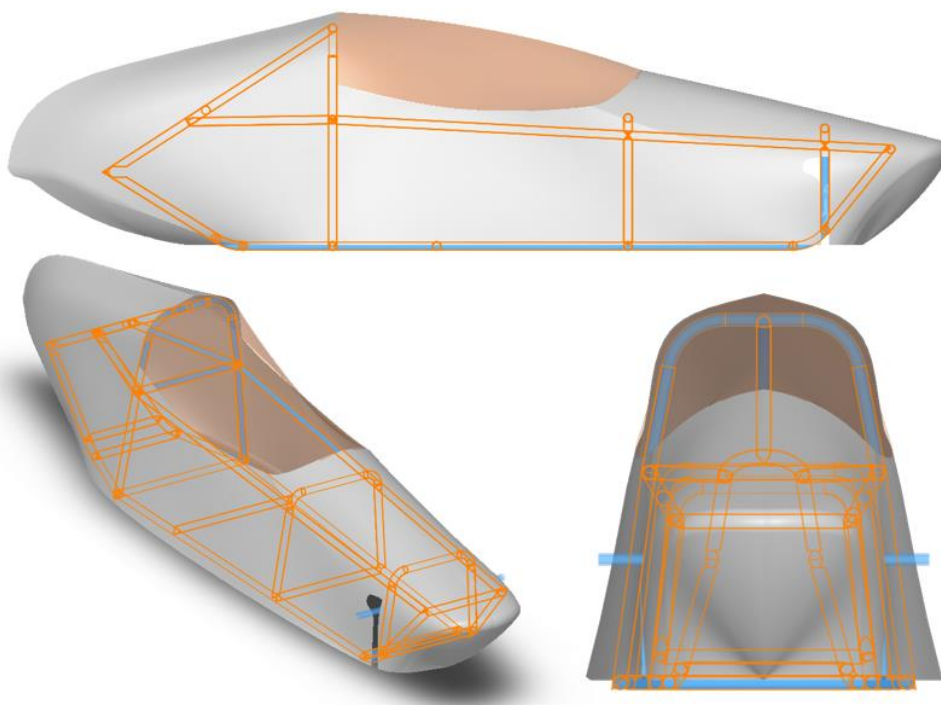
Carroceria envolvendo o chassi, vistas lateral, isométrica e frontal.
